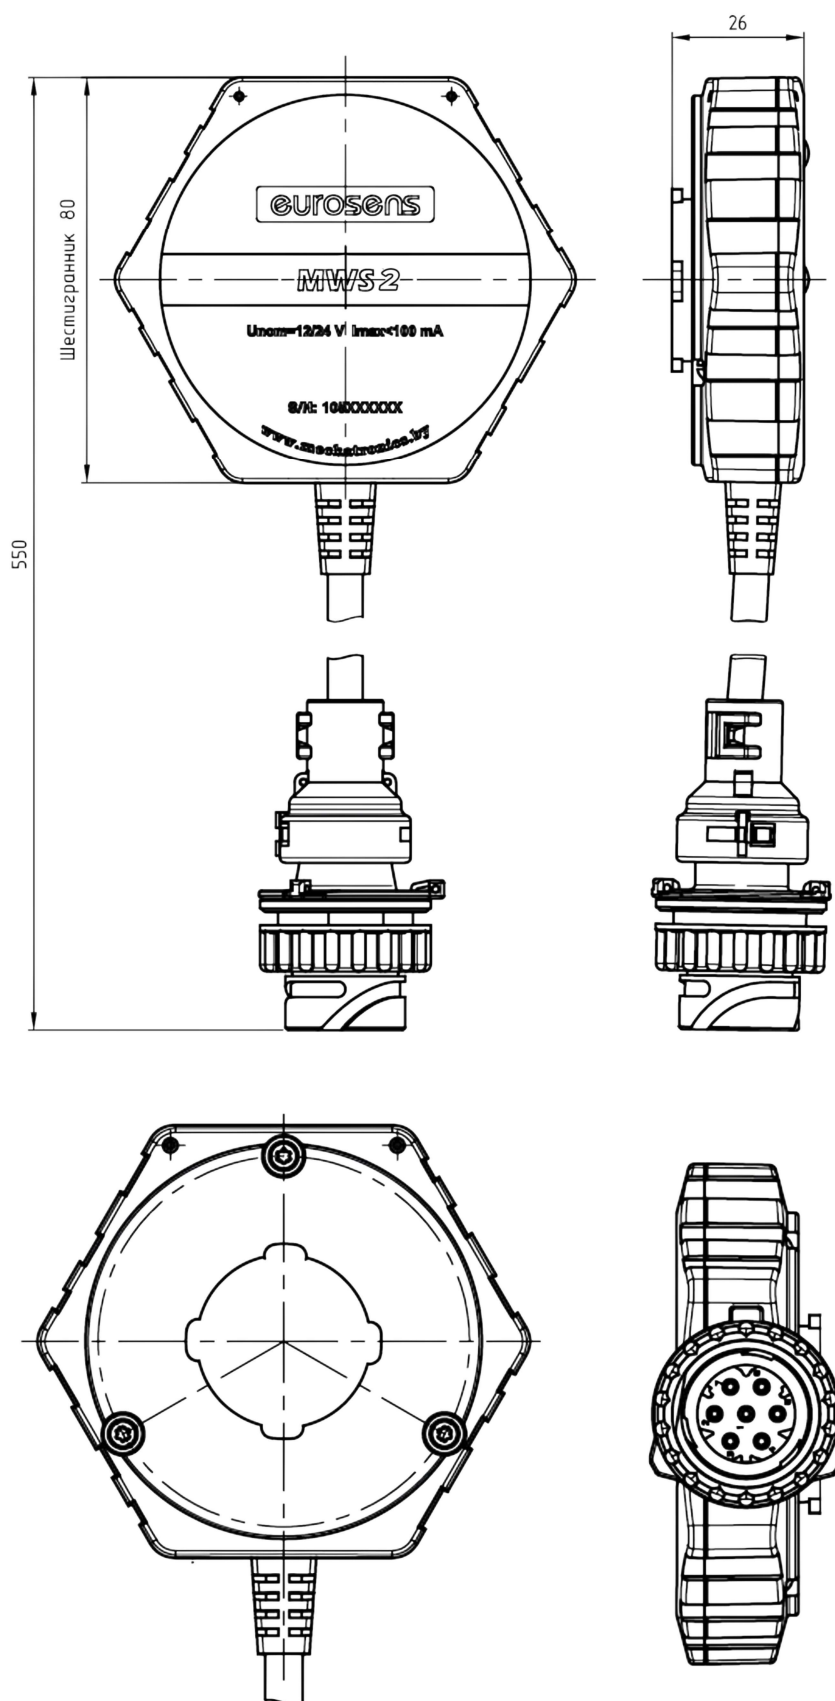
Габаритный чертеж датчика eurosens MWS 2
